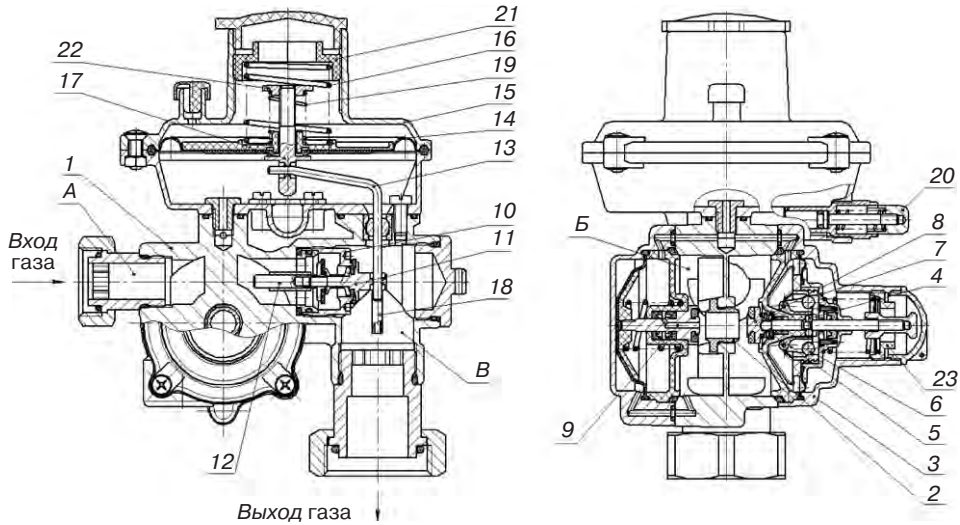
Схема принципиальной работы регулятора давления РДГБ-10(25): А — входная камера; В — промежуточная камера; В — выходная камера; 1 — корпус; 2 — седло; 3 — отключающее устройство; 4 — фиксирующие шарики; 5 — передаточные рычаги; 6 — ролики; 7 — мембранный узел; 8 — клапан; 9 — сервопривод первой ступени редуцирования; 10 — седло регулирующего клапана второй ступени; 11 — сдвоенный регулирующий и запорный клапан; 12 — шток; 13 — рычажный передаточный механизм; 14 — рабочая мембрана; 15 — корпус; 16 — задающая пружина; 17 — сбросной клапан; 18 — импульсная трубка; 19 — пружина; 20 — кнопка запуска; 21, 22, 23 — гайки регулировочные
